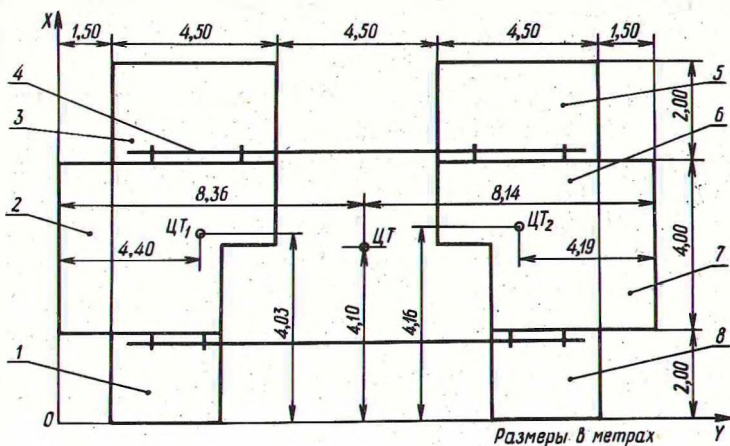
Центр тяжести машины БТИ-2В: 1 – дополнительный понтон; 2 – основной понтон с двигателем; 3 – дополнительный понтон; 4 – стяжная труба; 5 – дополнительный понтон; 6 – основной понтон со станком намотки проволоки; 7 – вынос для балластного груза; 8 – дополнительный понтон.
